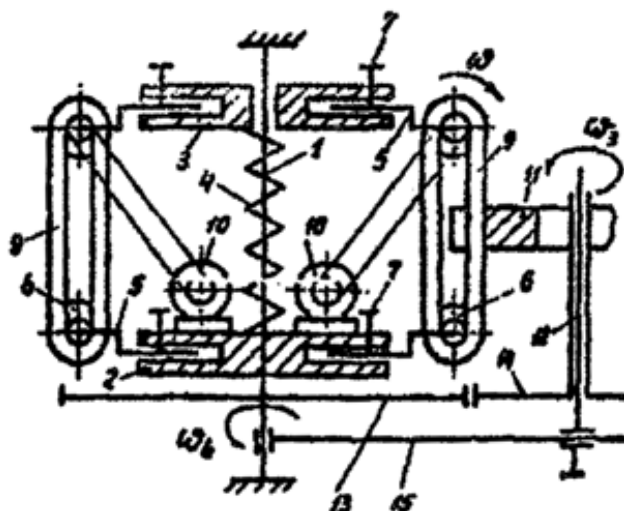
Планетарная схема устройства для обработки впадин зубчатых колес (15-водило).
